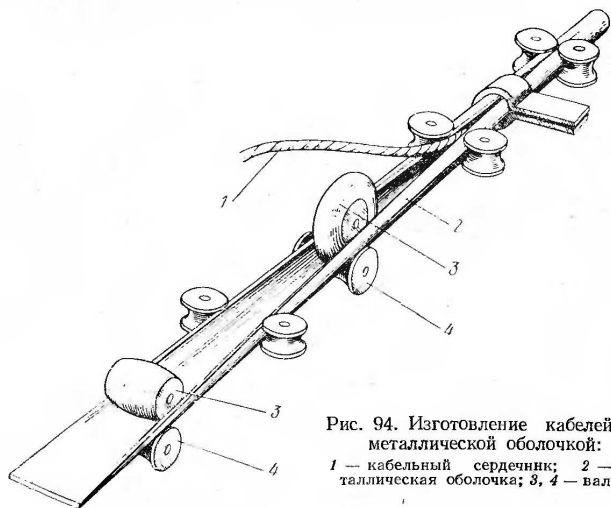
Изготовление кабелей с металлической оболочкой:
